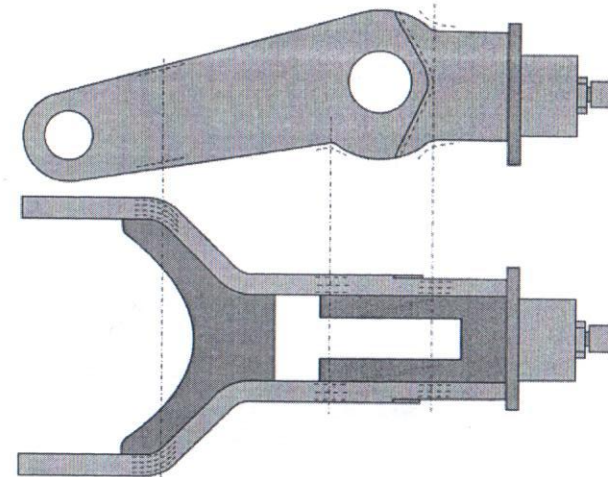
Контроль околошовных зон сварных соединений деталей рычага
